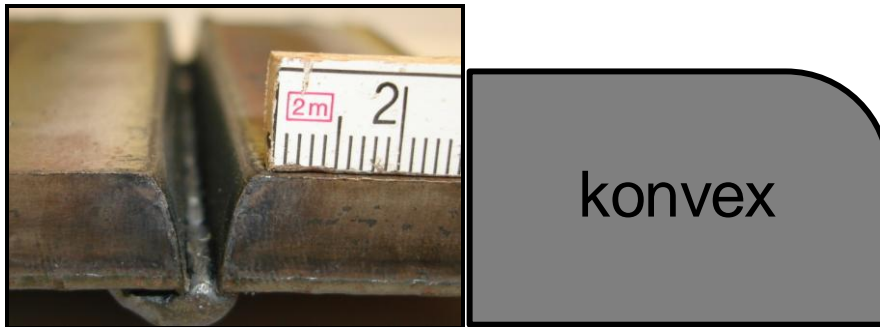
Konvexe Schnittoberkante durch Wirbelgasverringering
